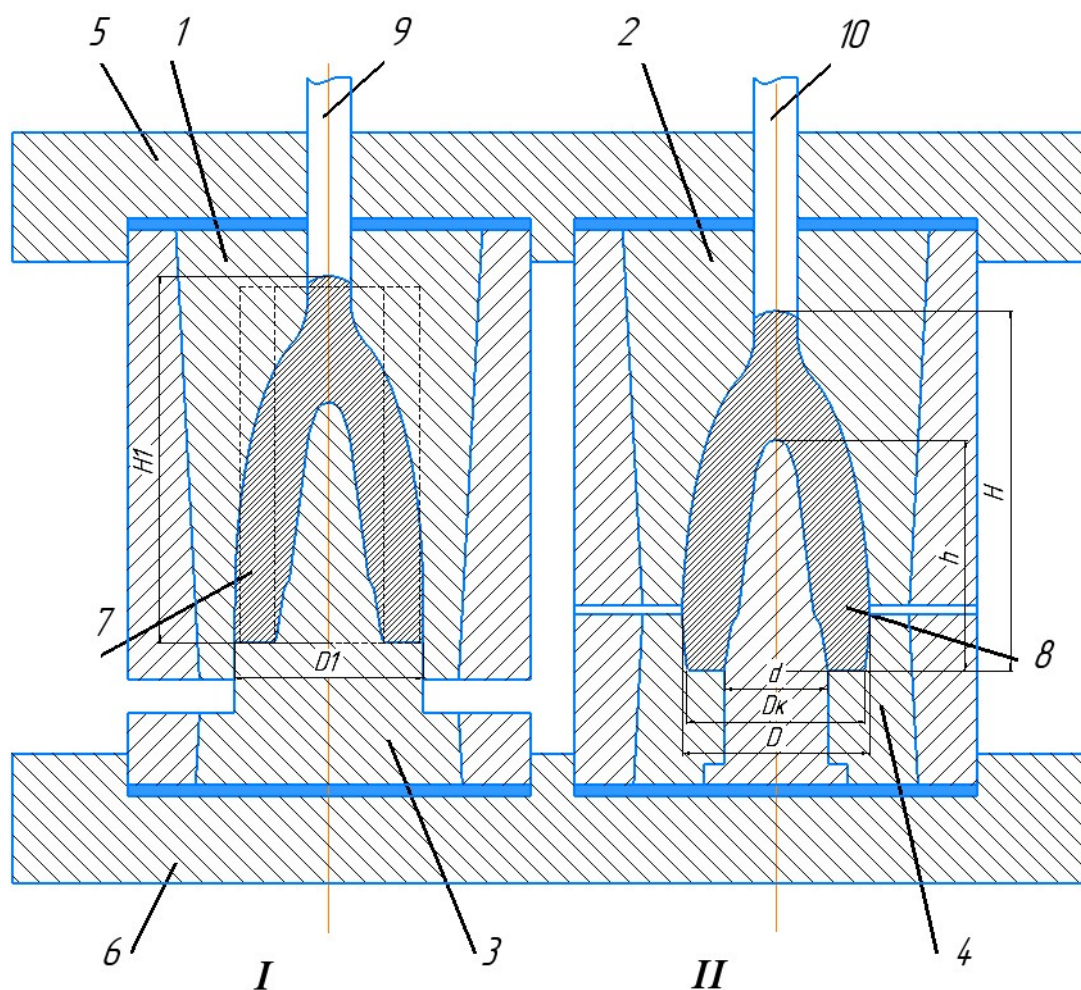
Штамп для горячей штамповки оправки $D=130$ мм, $H=250$ мм из трубной заготовки $D_z=116 \times 271$ мм
